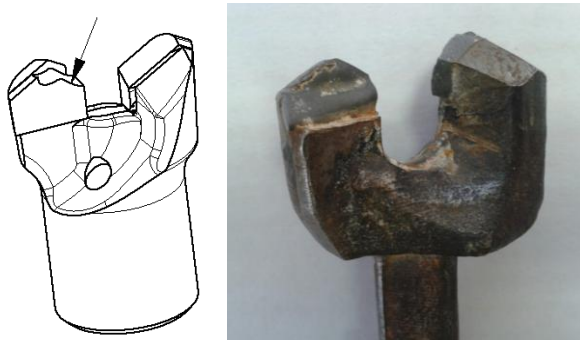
Буровой резец со сколом режущей кромки пластины
